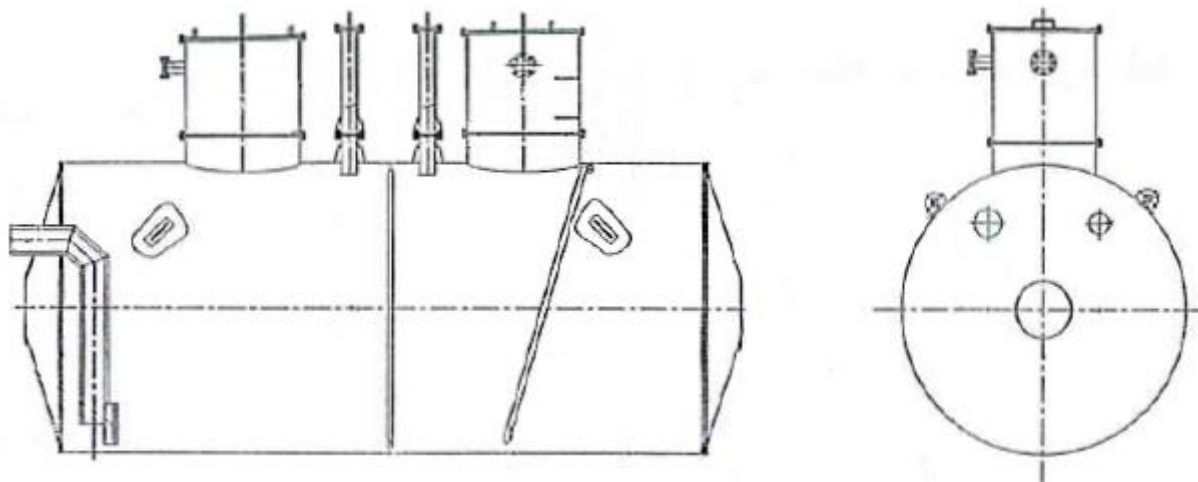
Общий вид эскиза резервуара РГС-40
